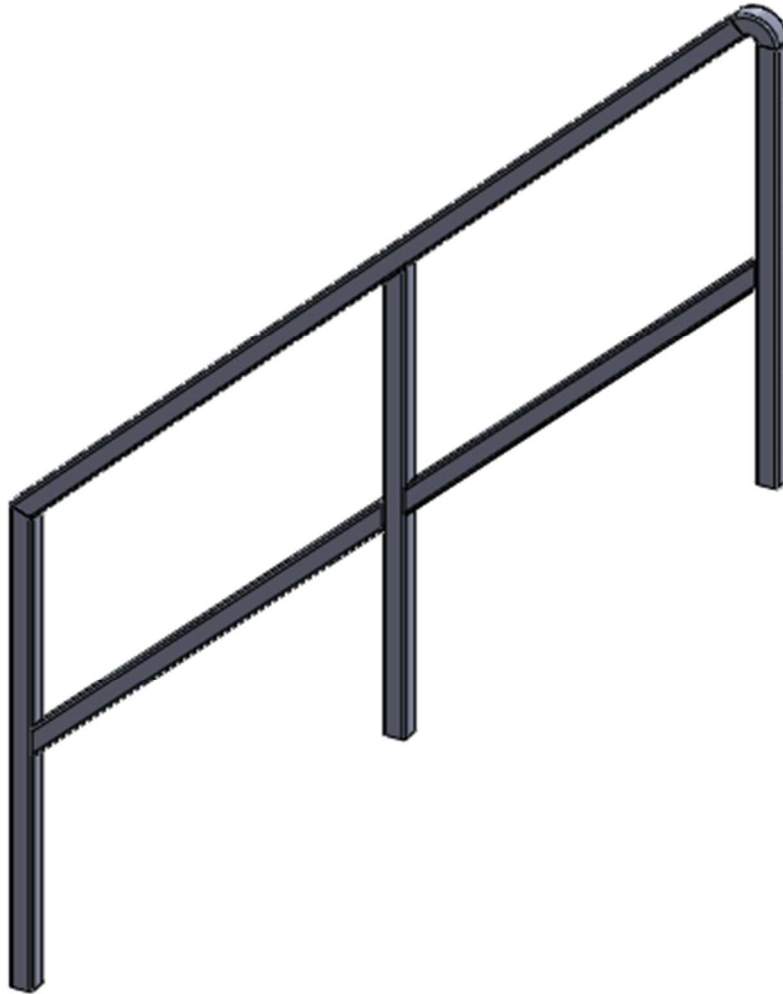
Baranda de las escaleras formada por perfiles ISO 30 x 30 x 2
